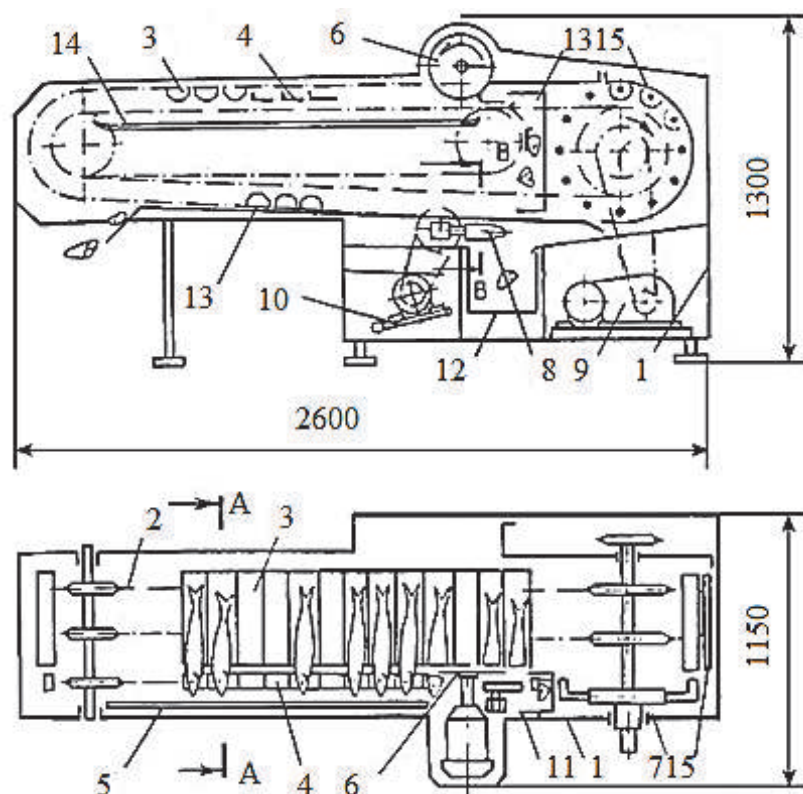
Общий вид машины рыбобороздочной ИРА-103М: 1 – станина; 2 – операционный транспортер; 3- лотки; 4 – лента сопровождения голов; 5 – ограничительная планка; 6 – ножевой механизм с индивидуальным приводом; 7 – гидроголовка; 8 – узел дозачистки внутренностей; 9 – привод операционного транспортера; 10 – привод; 11, 12 – лотки отвода голов; 13 – поддон; 14 – узел дозачистки внутренностей; 18 – пружина; 19 – направляющая
